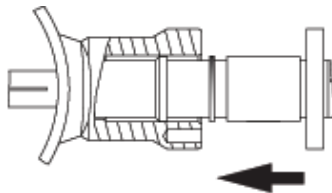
Уплотнительное кольцо, детальный чертеж
